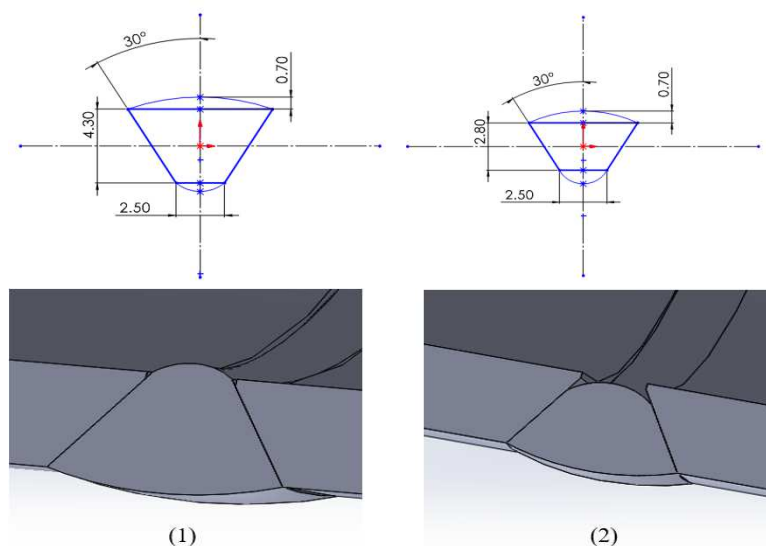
Le joint soudé (1) le joint parfait (2) le joint défectueux
